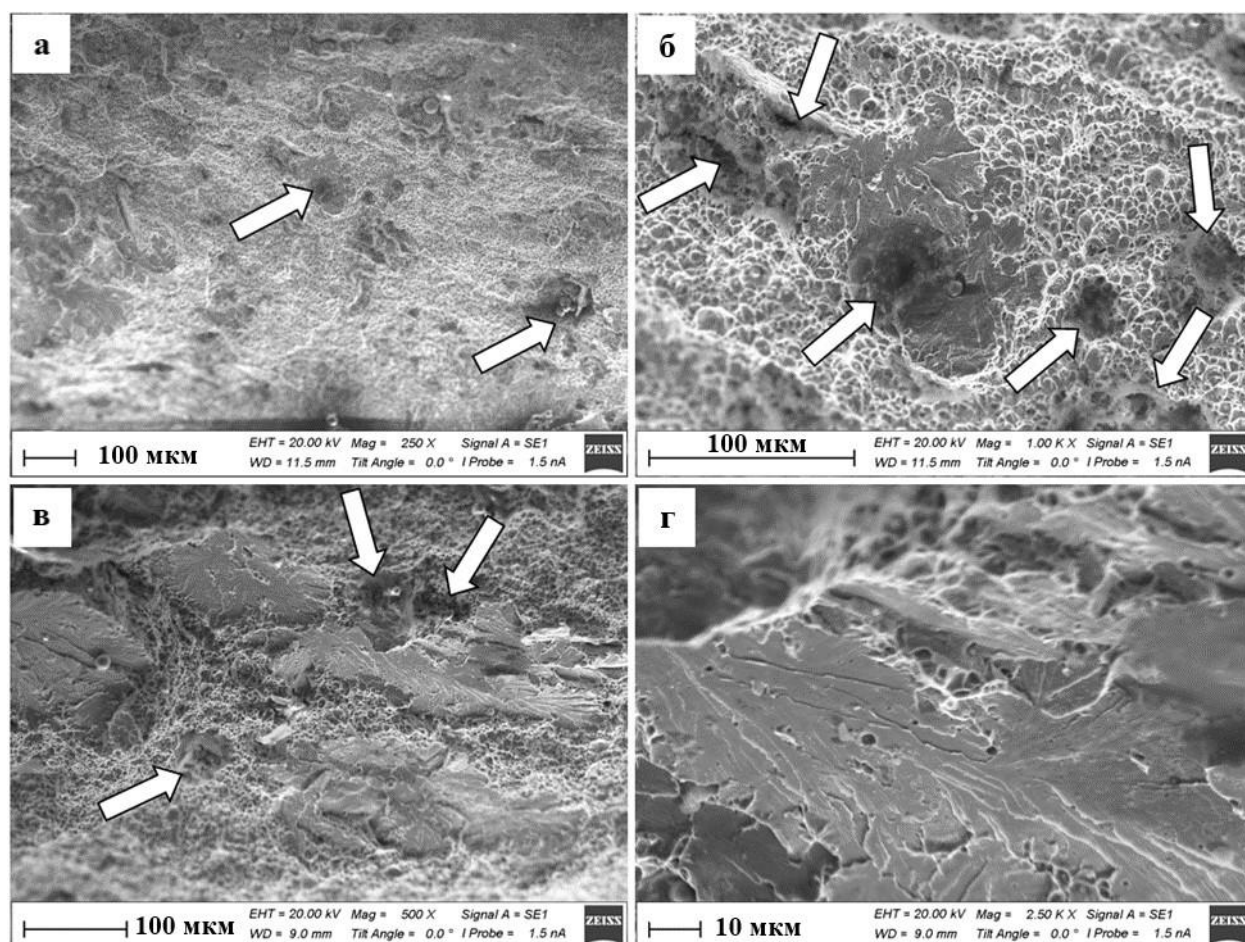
Электронно-микроскопическое изображение поверхности излома металла наплавки (стрелками указаны микро- и макропоры, несплошности металла)
